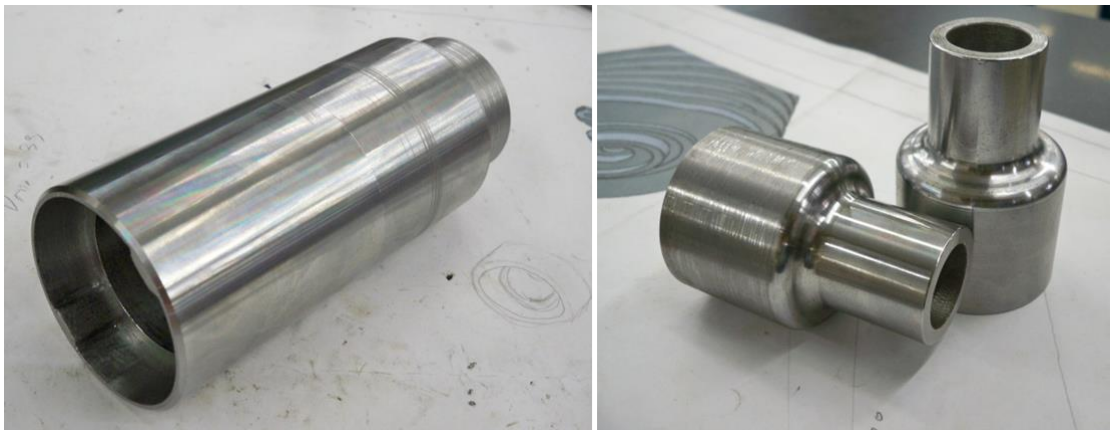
Maquinado del eje conducido en un Torno CNC
